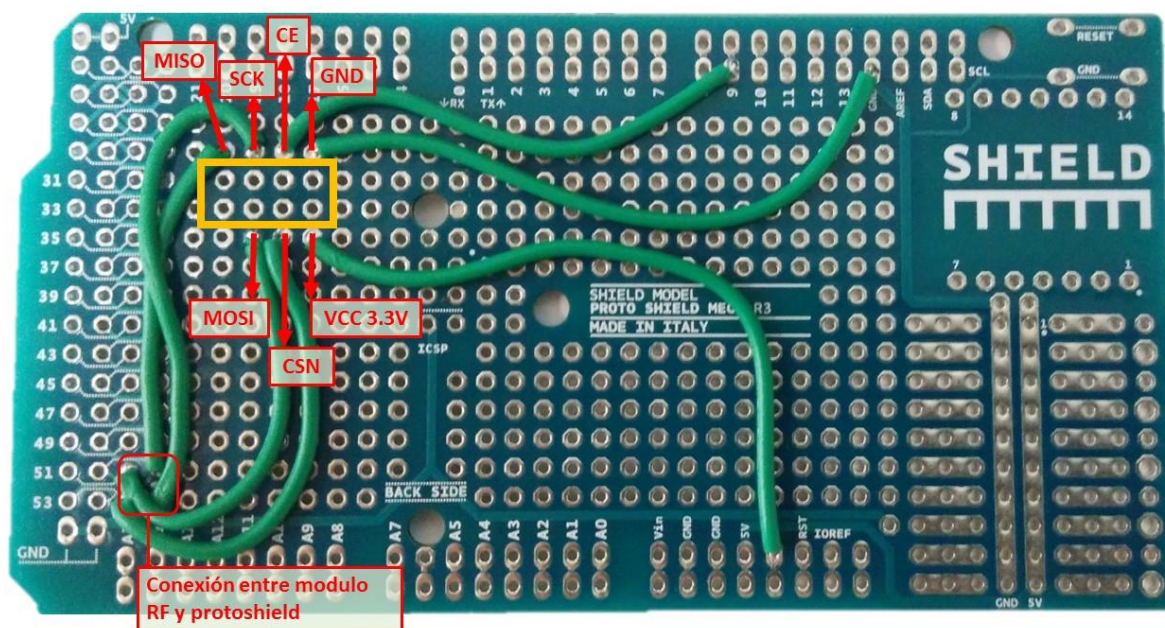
Cara interior de la protoshield con el cableado soldado (Fuente:propia)
